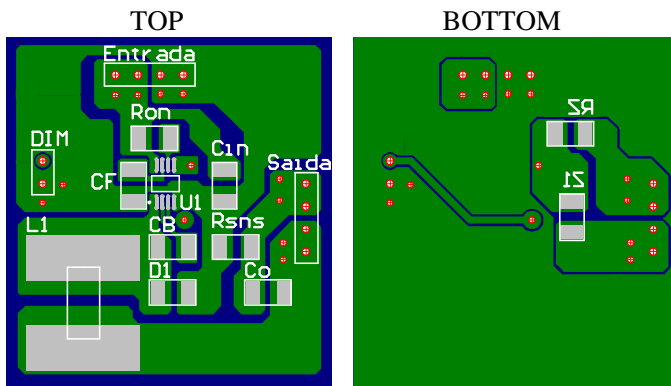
Layout da placa de circuito impresso do conversor com o LM 3402.
